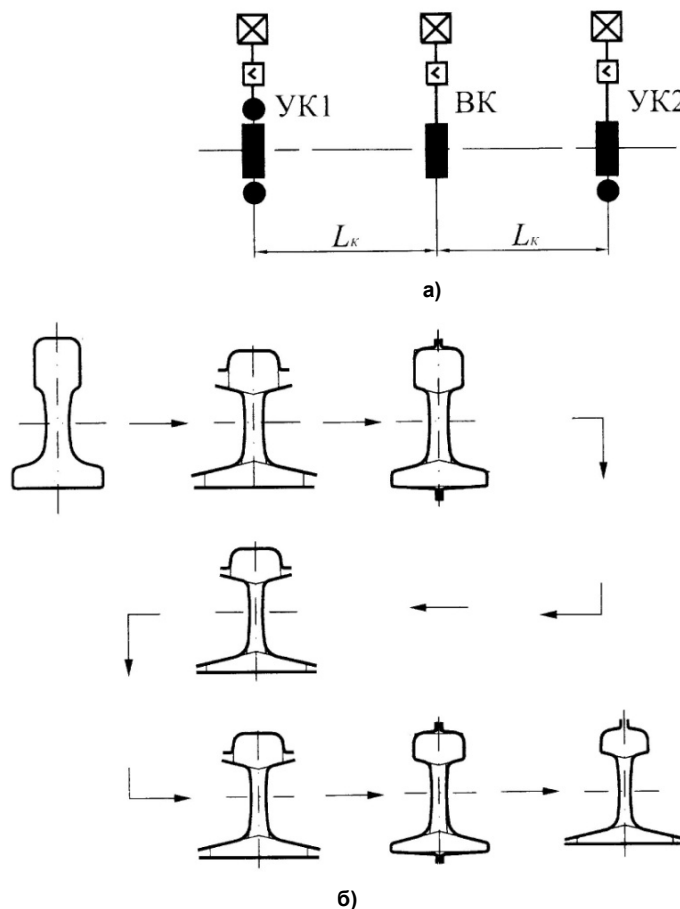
Расположение рабочих клеток (а) и схема прокатки рельсов (б) в непрерывно-реверсивной группе современного рельсобалочного стана
